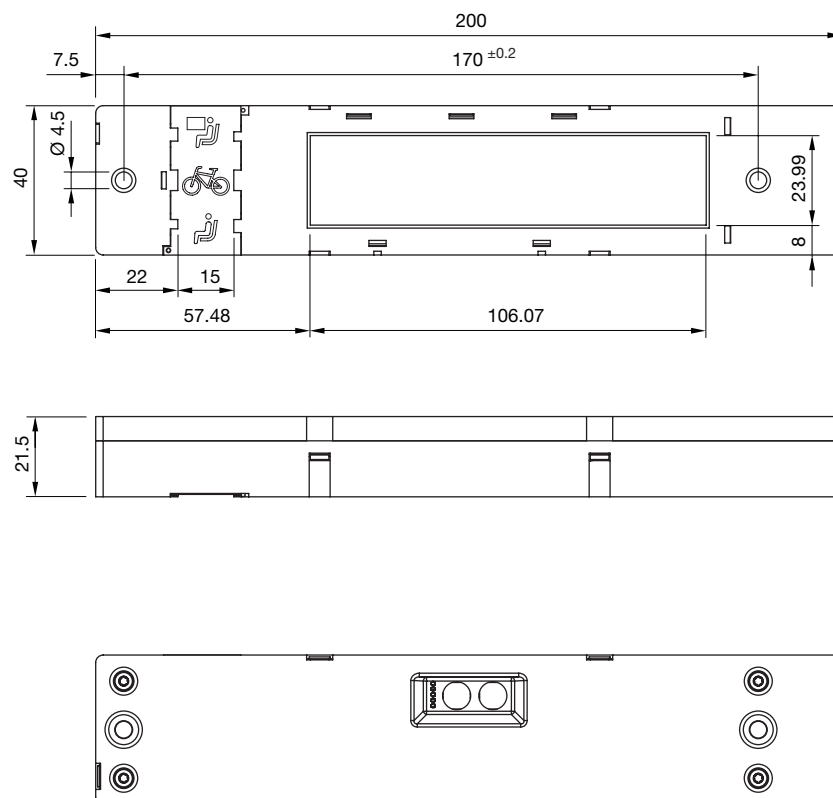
Abmessungen (mm) Gehäuse Schraub-Befestigung.
